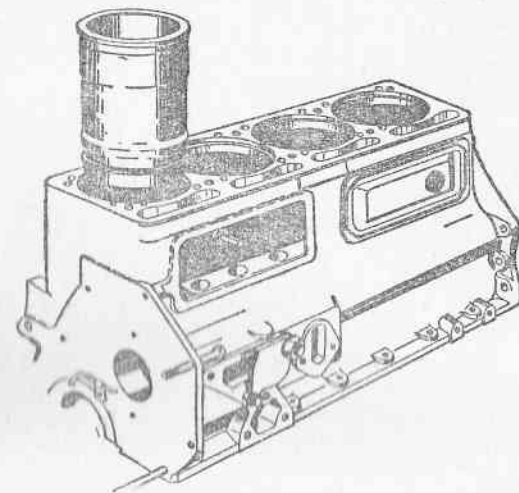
Блок цилиндров двигателя М-21 «Волга».
